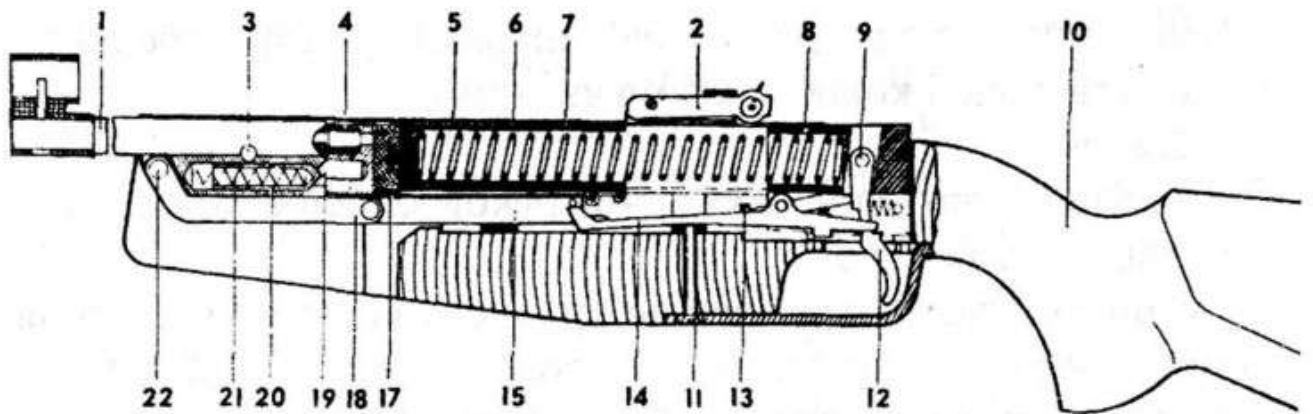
Механизмы пневматической винтовки ИЖ-38С: 1 - ствол; 2 - прицел; 3 - ось ствола; 4 - прокладка ствола; 5 - коробка ствольная; 6 - поршень; 7 - пружина боевая; 8 - колодка механизма спускового; 9 - штифт колодки; 10 - ложка; 11 - винт ложки задней; 12 - крючок спусковой; 13 - шептало; 14 - рычаг блокировки; 15 - рычаг взведения; 17 - манжета; 18 - шарнир; 19 - клин; 20 - ригель; 21 - пружина ригеля; 22 - ось шарнира.
